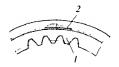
Шлифовальный шевер с внутренними зубьями:
